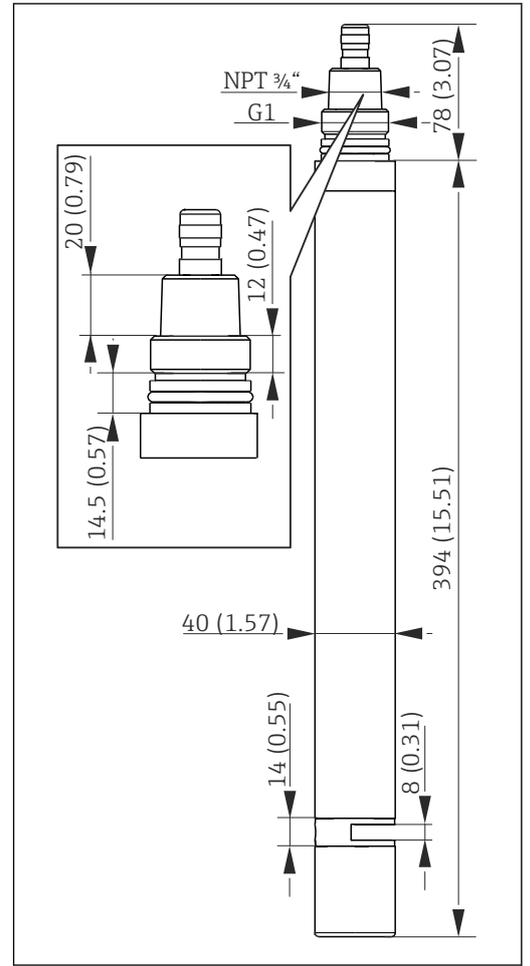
8 mm (0.31 in) 光程的传感器的外形尺寸示意图; 单位: mm (in)
